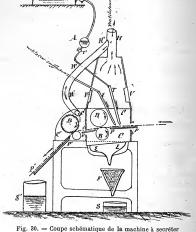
Coupe schématique de la machine à secréter de MM. Pichard frères.
